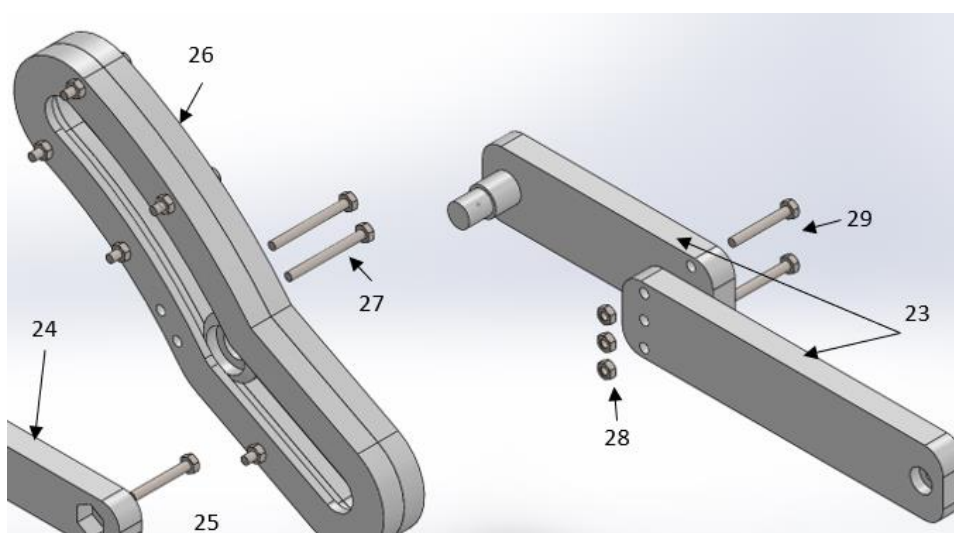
Explosión ensamble eslabón seguidor y dispositivo deslizador.
